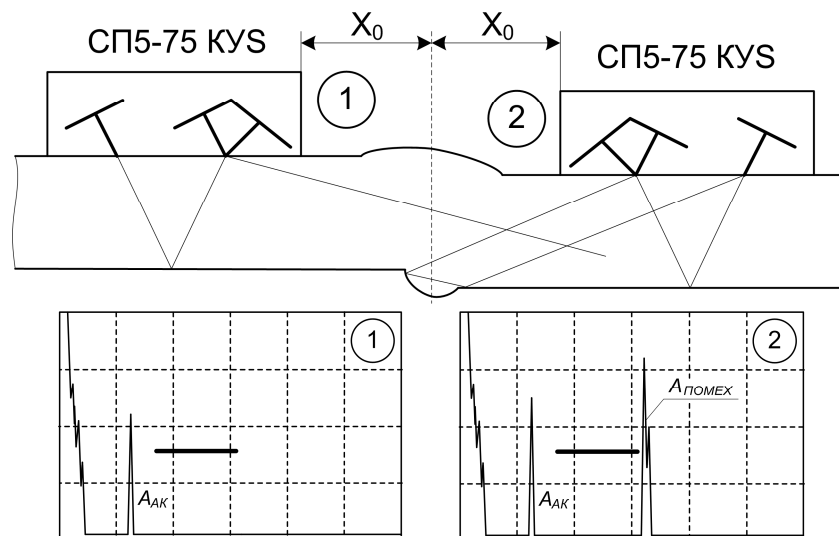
УЗК стыкового сварного соединения со смещением кромок.
